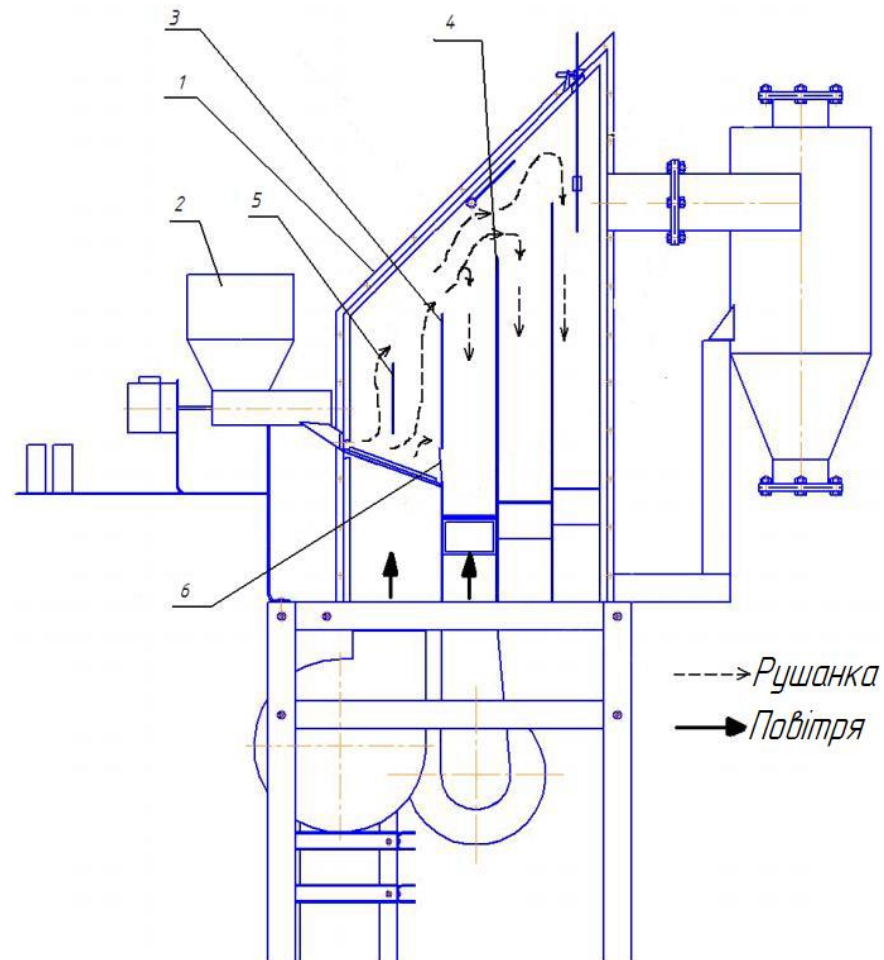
Схема лабораторно-експериментального пневмосепаратора для поділу зернового матеріалу: 1 – корпус; 2 – шнековий дозатор; 3 – задня стінка сепаруючого каналу; 4 – стінка осаджувального каналу; 5 – бар'єр, що вирівнює зерновий потік; 6 – перегородка
